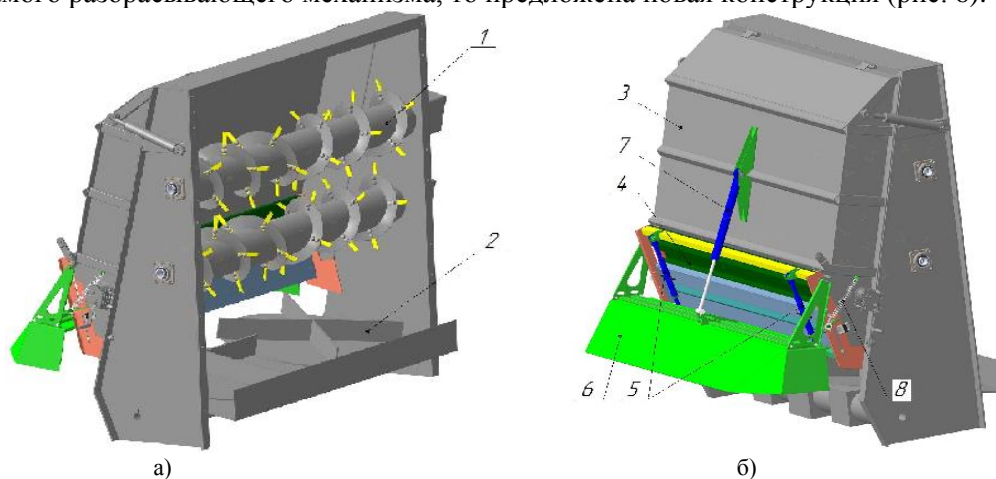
Схема комбинированного рабочего органа для внесения мелиорантов: а) вид сзади; б) вид спереди; 1 – фрезерный агрегат; 2 – дисковый распределитель; 3 – клапан; 4 – предохранительный щиток; 5 – талрепы; 6 – ограничитель распределения; 7 – гидроцилиндр; 8 – пружины предохранительные
